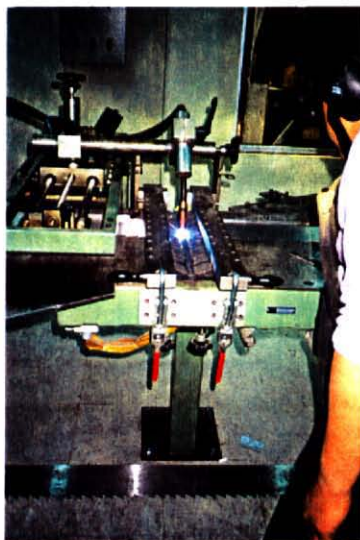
EQUIPO SOLDADOR (método de protección gaseosa).
